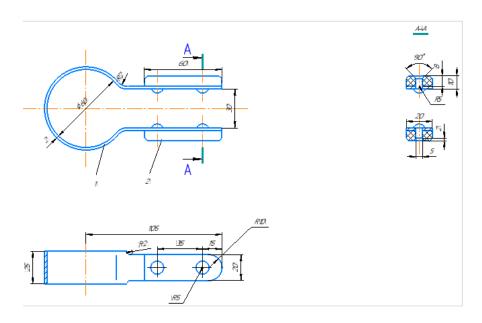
Приспособление для установки поршней в цилиндры компрессора
